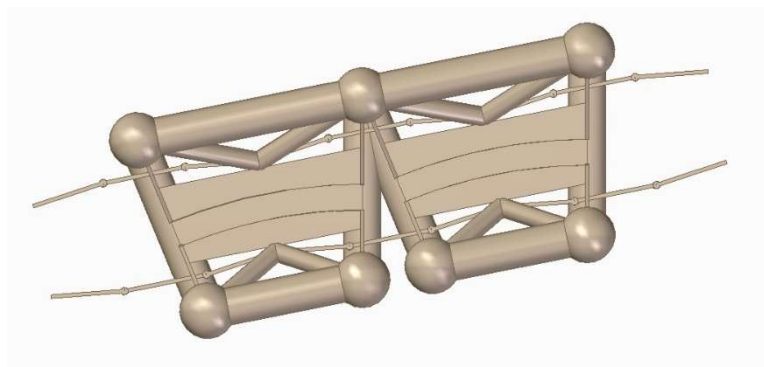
Piezas articuladas guía poligonal (Alzado)
